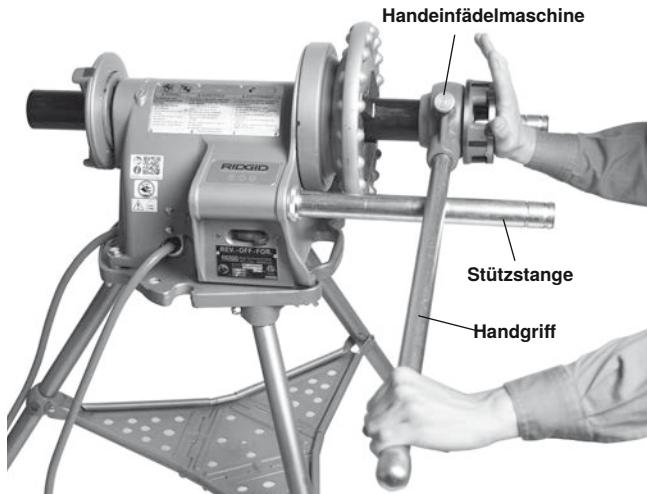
Schieben der Handgewindeschneidmaschine auf das Rohr zum Einrasten der Schneidbacken
